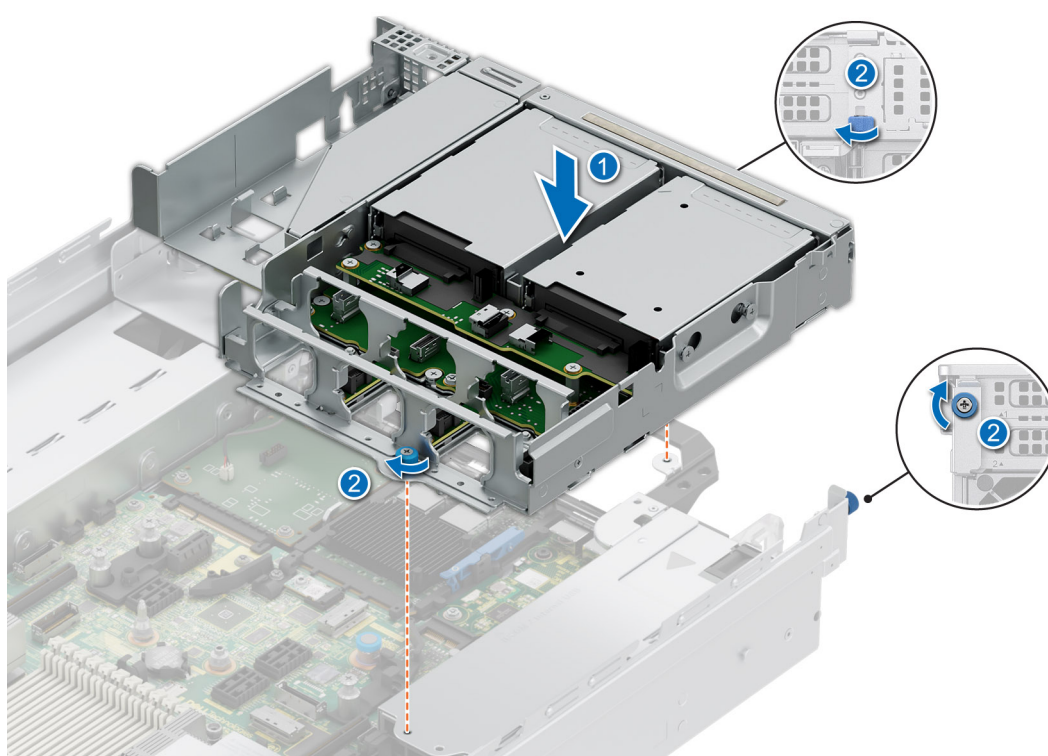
Installation du module de disques arrière 4 x 2,5 pouces
